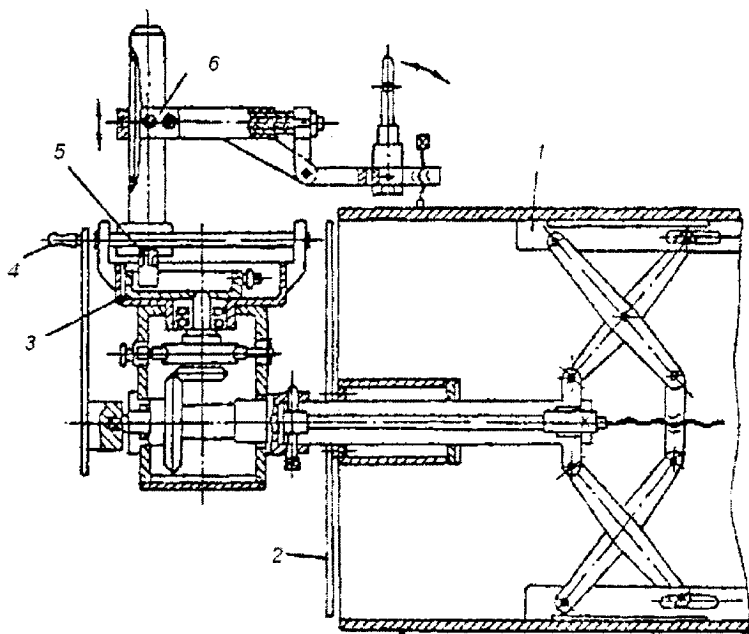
Пристрій ПРТ-1 для газового різання кінців сталевих труб:
